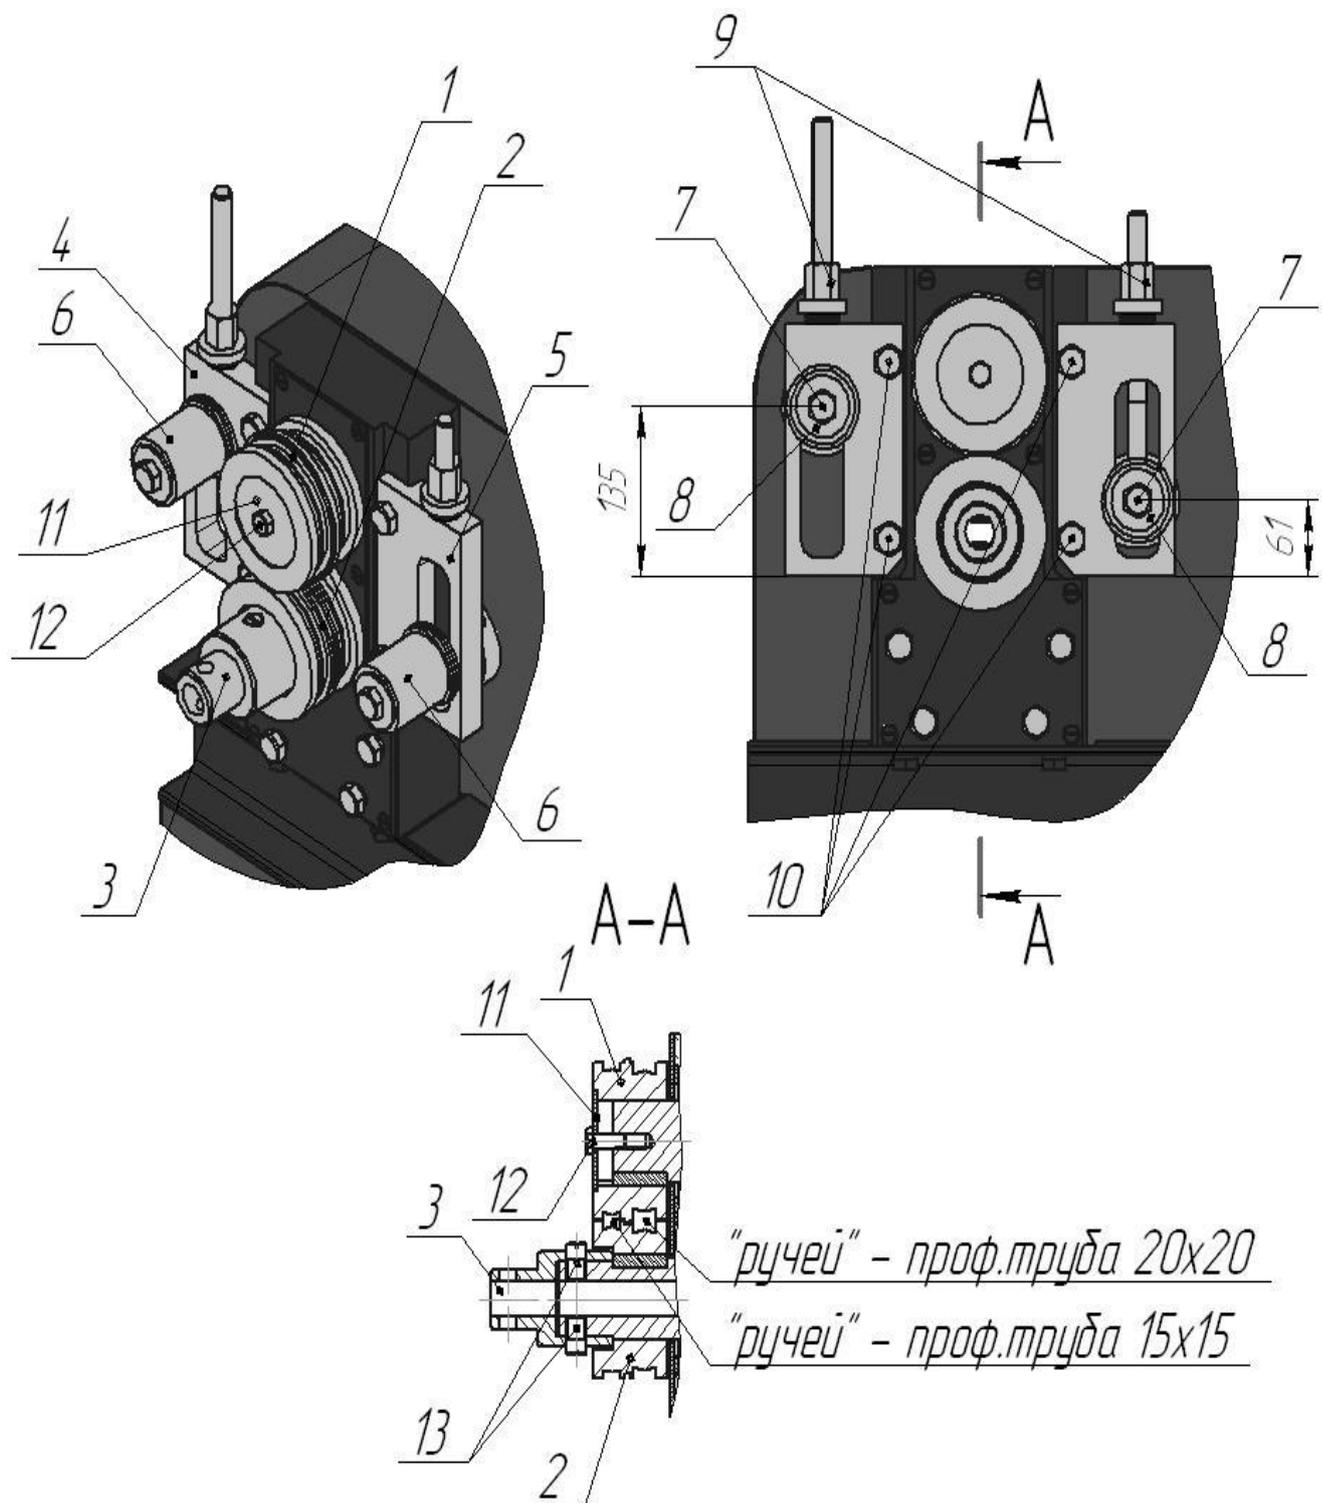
Монтаж дополнительных приспособлений для операции по усилению полосы (изготовление заготовок для хомутов).
